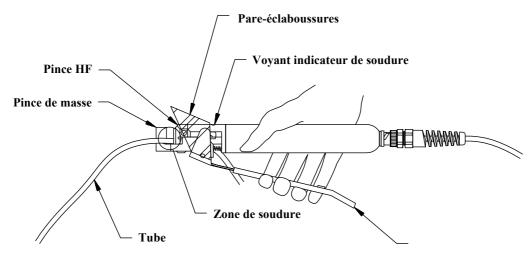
Technique adéquate de maintien de la tête de soudure
